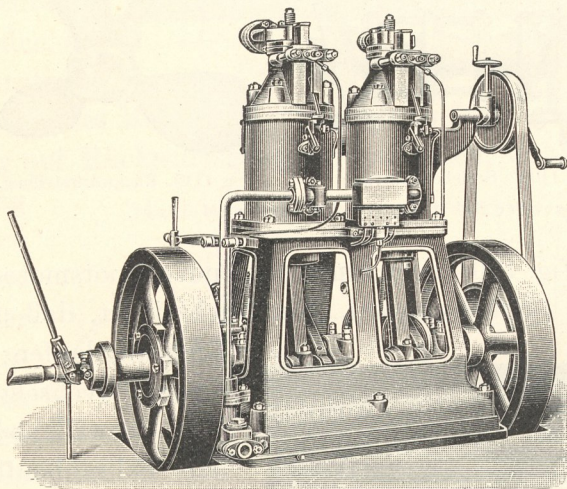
Stehender Bootsmotor (Zwillingmotor).
